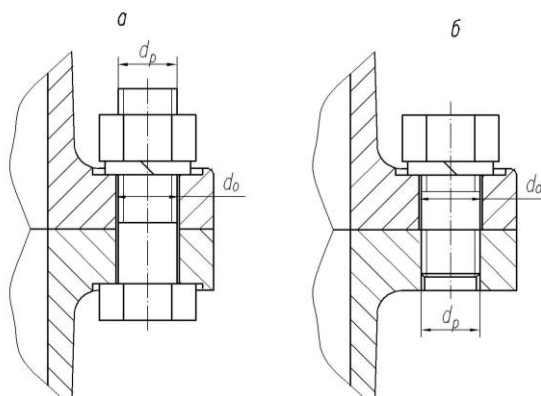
Варианты крепления крышки и основания корпуса редуктора
